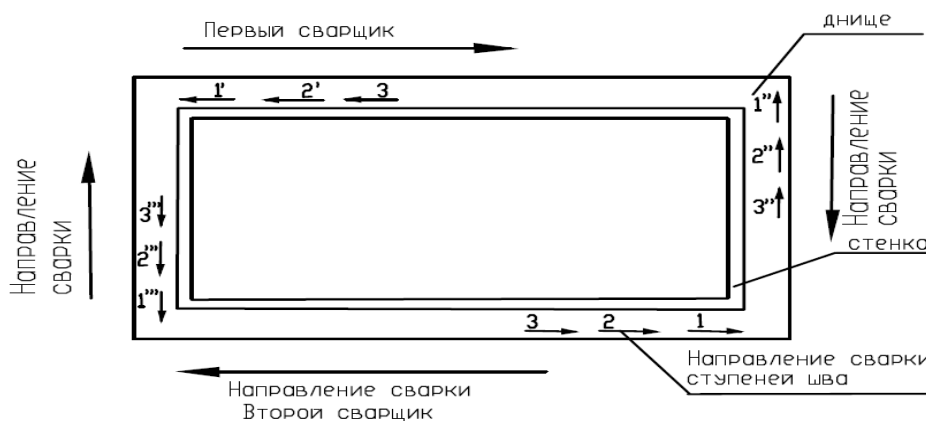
Последовательность сварки соединений прямоугольных конструкций
